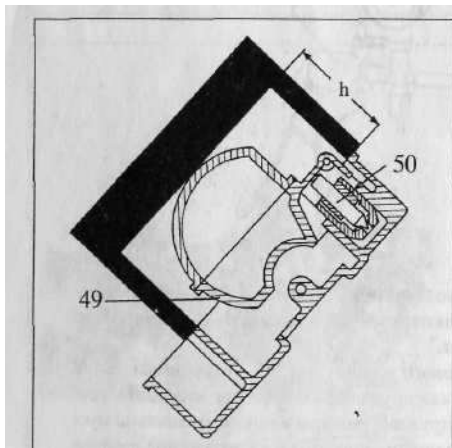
Регулировка положения кулачка пускового устройства.
